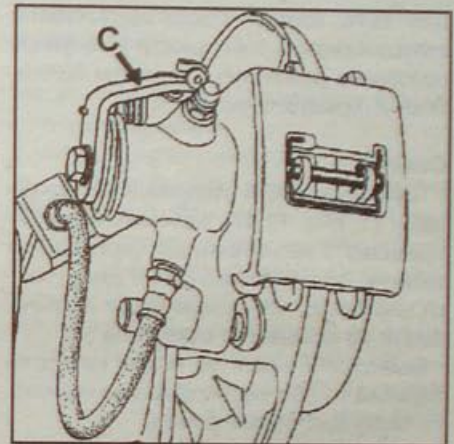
Расположение рычага (С) привода стояночного тормоза на автомобилях с задними дисковыми тормозами
